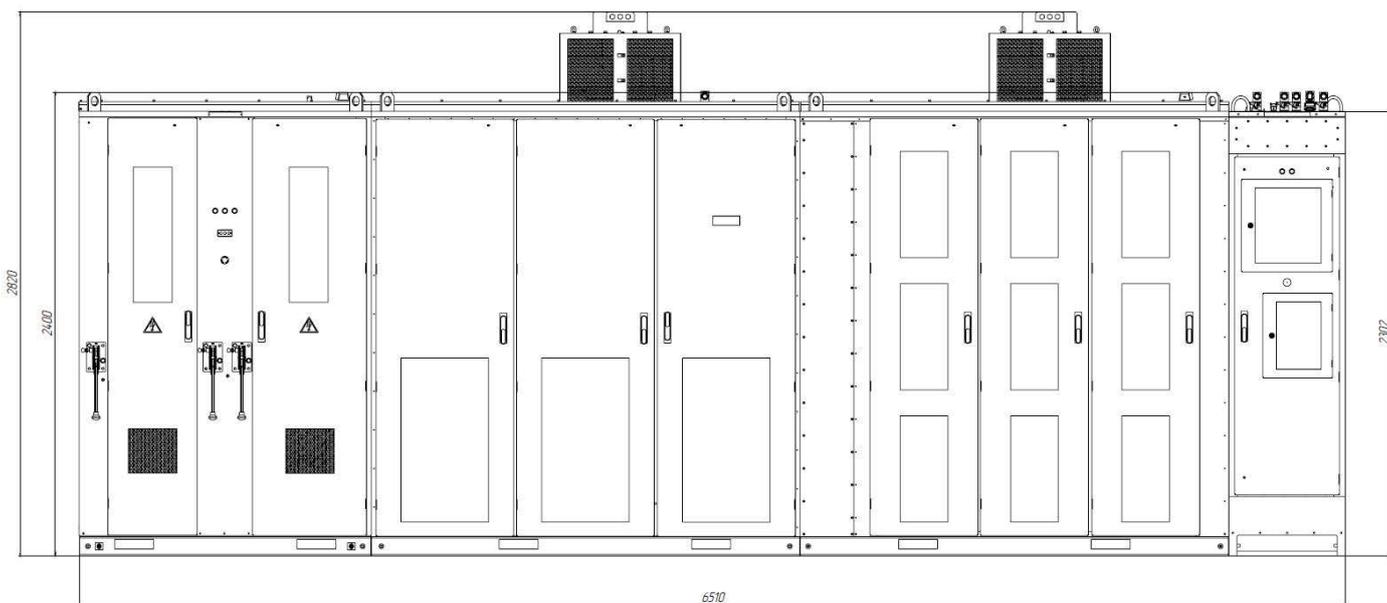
АТ27-М80...1М6-6/6-XXXXXX-С-43. Вид спереди
